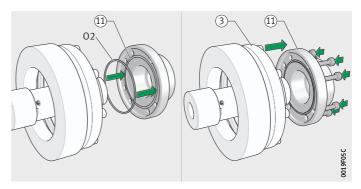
将 0 型圈 02 和刚性齿轮安装在相 邻结构上
